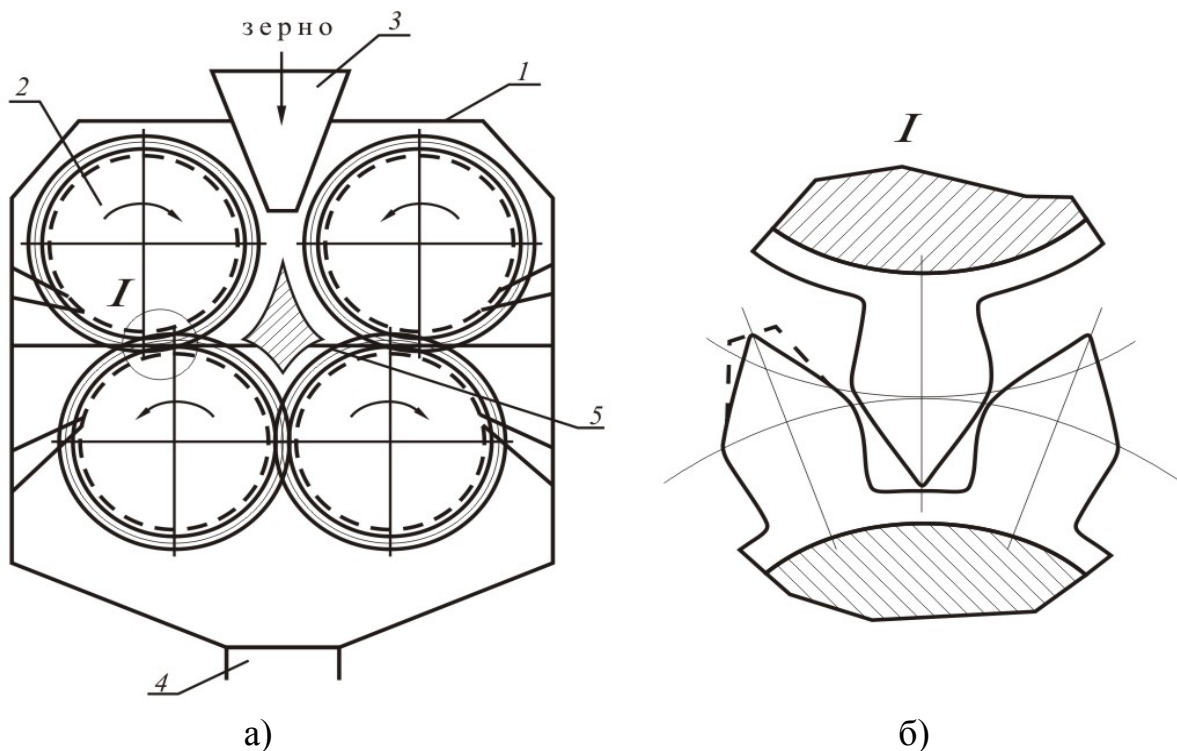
Пристрій для подрібнення зерна: 1 - корпус; 2 - валки; 3 - завантажувальний отвір; 4 - патрубок відводу; 5 – порожнина
